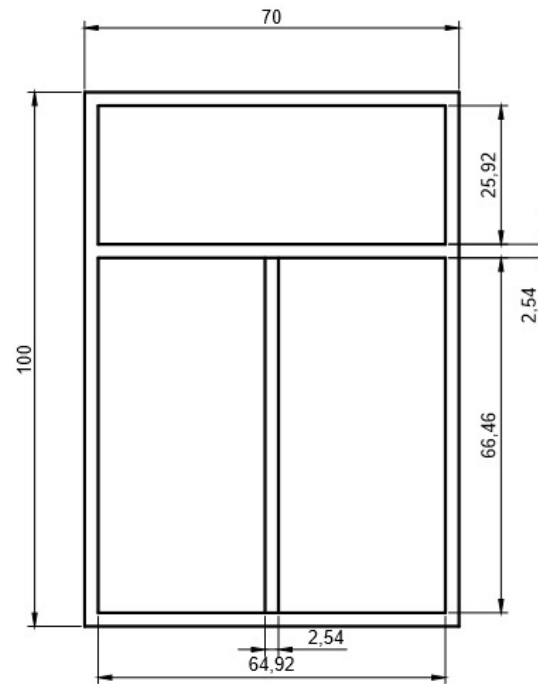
Vista frontal de estructura con dimensiones en centímetros
